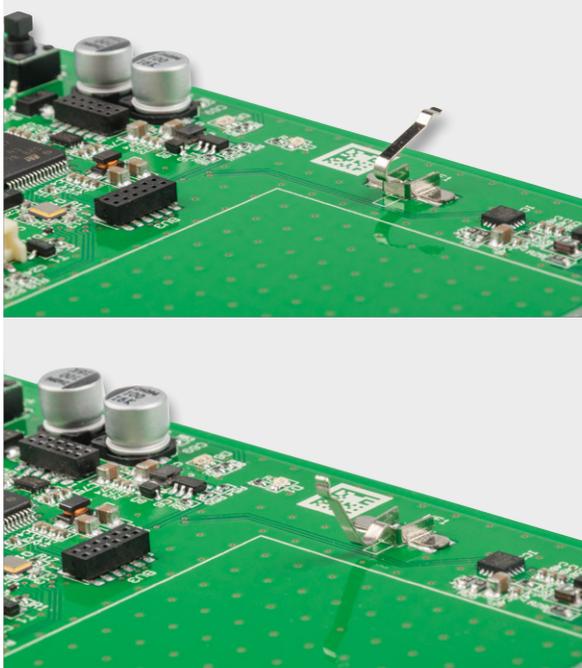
Biegen der Kontaktfeder KF1 in die endgültige Position
